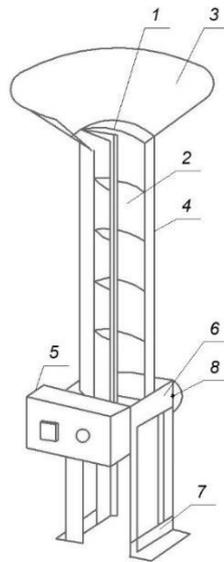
Пристрій для знезараження зерна: 1 – електропровідний стрижень; 2 – діелектричні лопатки; 3 – завантажувальний бункер; 4 – циліндрична труба; 5 – генератор високої напруги; 6 – корпус; 7 – кріплення; 8 – вібратор [3].
